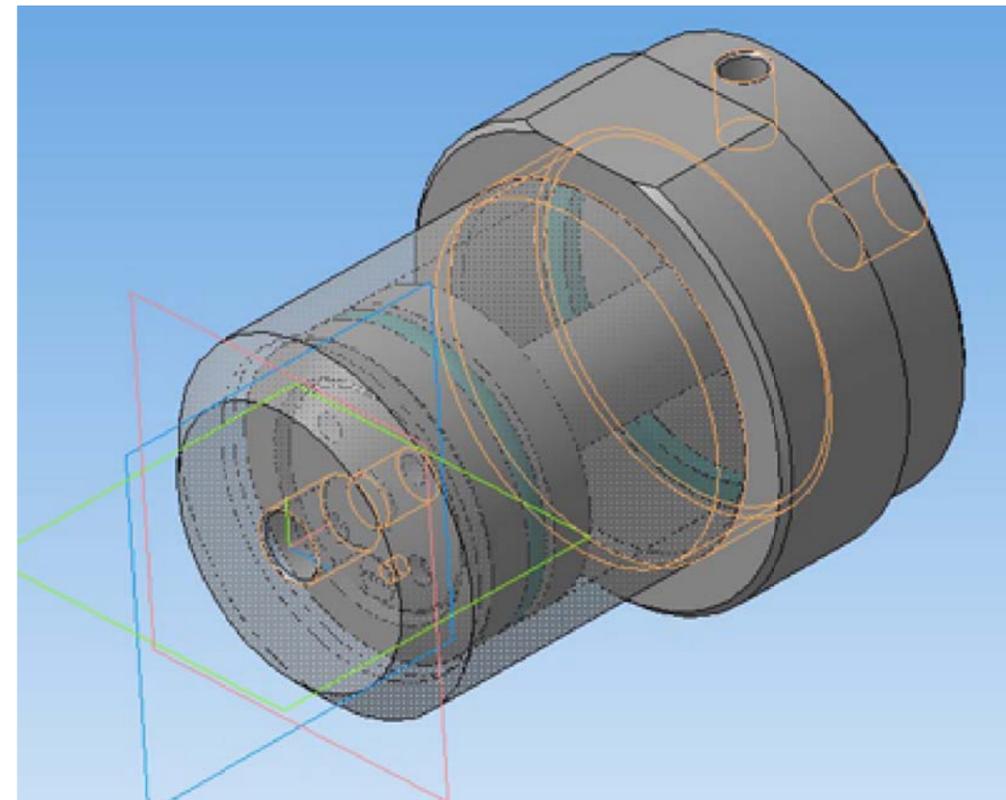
Трехмерное полупрозрачное изображение цилиндра пневматического
